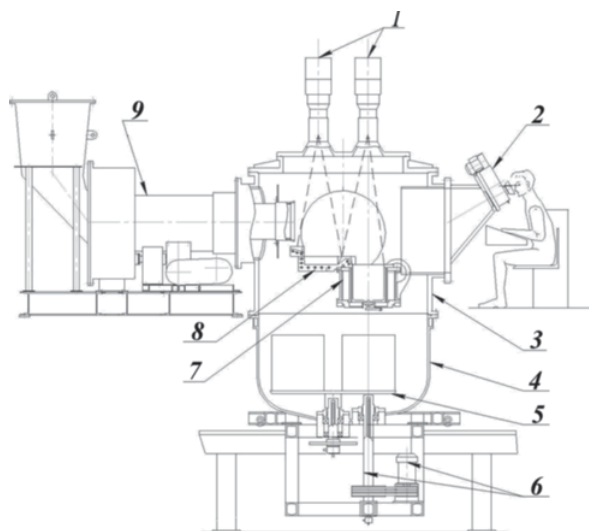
Схема электронно-лучевой установки для центробежного литья: 1 – пушки ВТР; 2 – смотровая система; 3 – плавильная камера; 4 – камера литейных форм; 5 – форма для центробежного литья; 6 – механизм вращения форм; 7 – гарнисажный тигель с СЭМП и донным сливом расплава; 8 – промежуточная емкость; 9 – устройство подачи шихты на переплав
